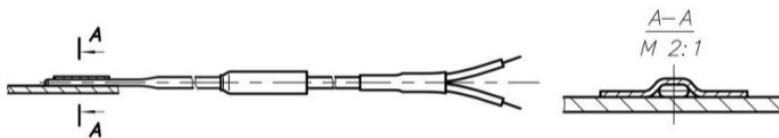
Способ монтажа датчика на основе КТМС на плоскую поверхность с помощью сварки
